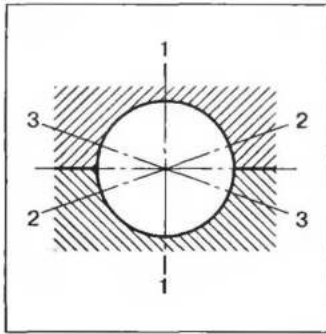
Схема измерения постели подшипника коленчатого вала: в плоскости 1-1 — основной размер; в плоскостях 2-2 и 3-3 — вспомогательные размеры для определения эллипсности постели и точности центрирования крышки
